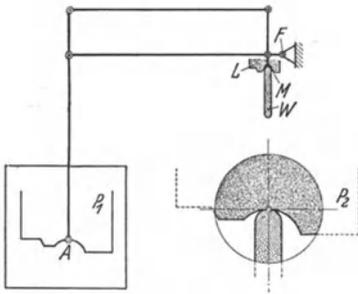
Prinzip einer optischen Profilschleifmaschine.
